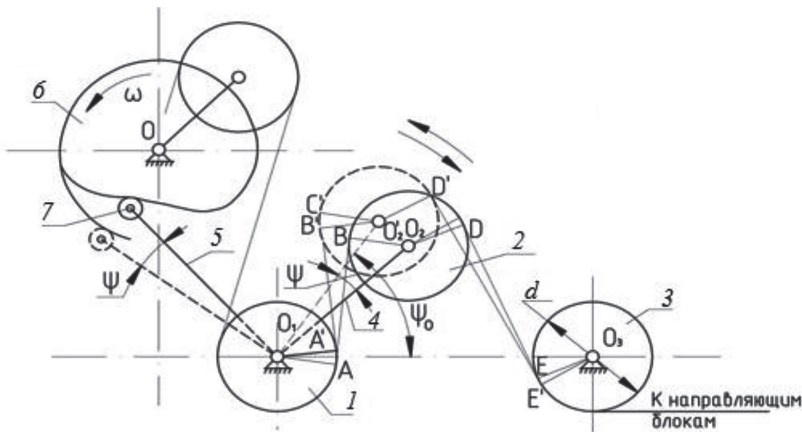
Схема дополнительного устройства для синхронизации перемещения приводных канатов пилы: 1, 3 — уравнивательные блоки с диаметром  $d$ ; 2 — вращающийся блок; 4 — двуплечий рычаг с короткими плечами; 5 — двуплечий рычаг с длинными плечами; 6 — кулачок; 7 — ролик;  $\Psi_0$  — угол между коромыслом и линией, соединяющей центра блоков 1 и 3;  $\Psi$  — текущий угол поворота коромысла
